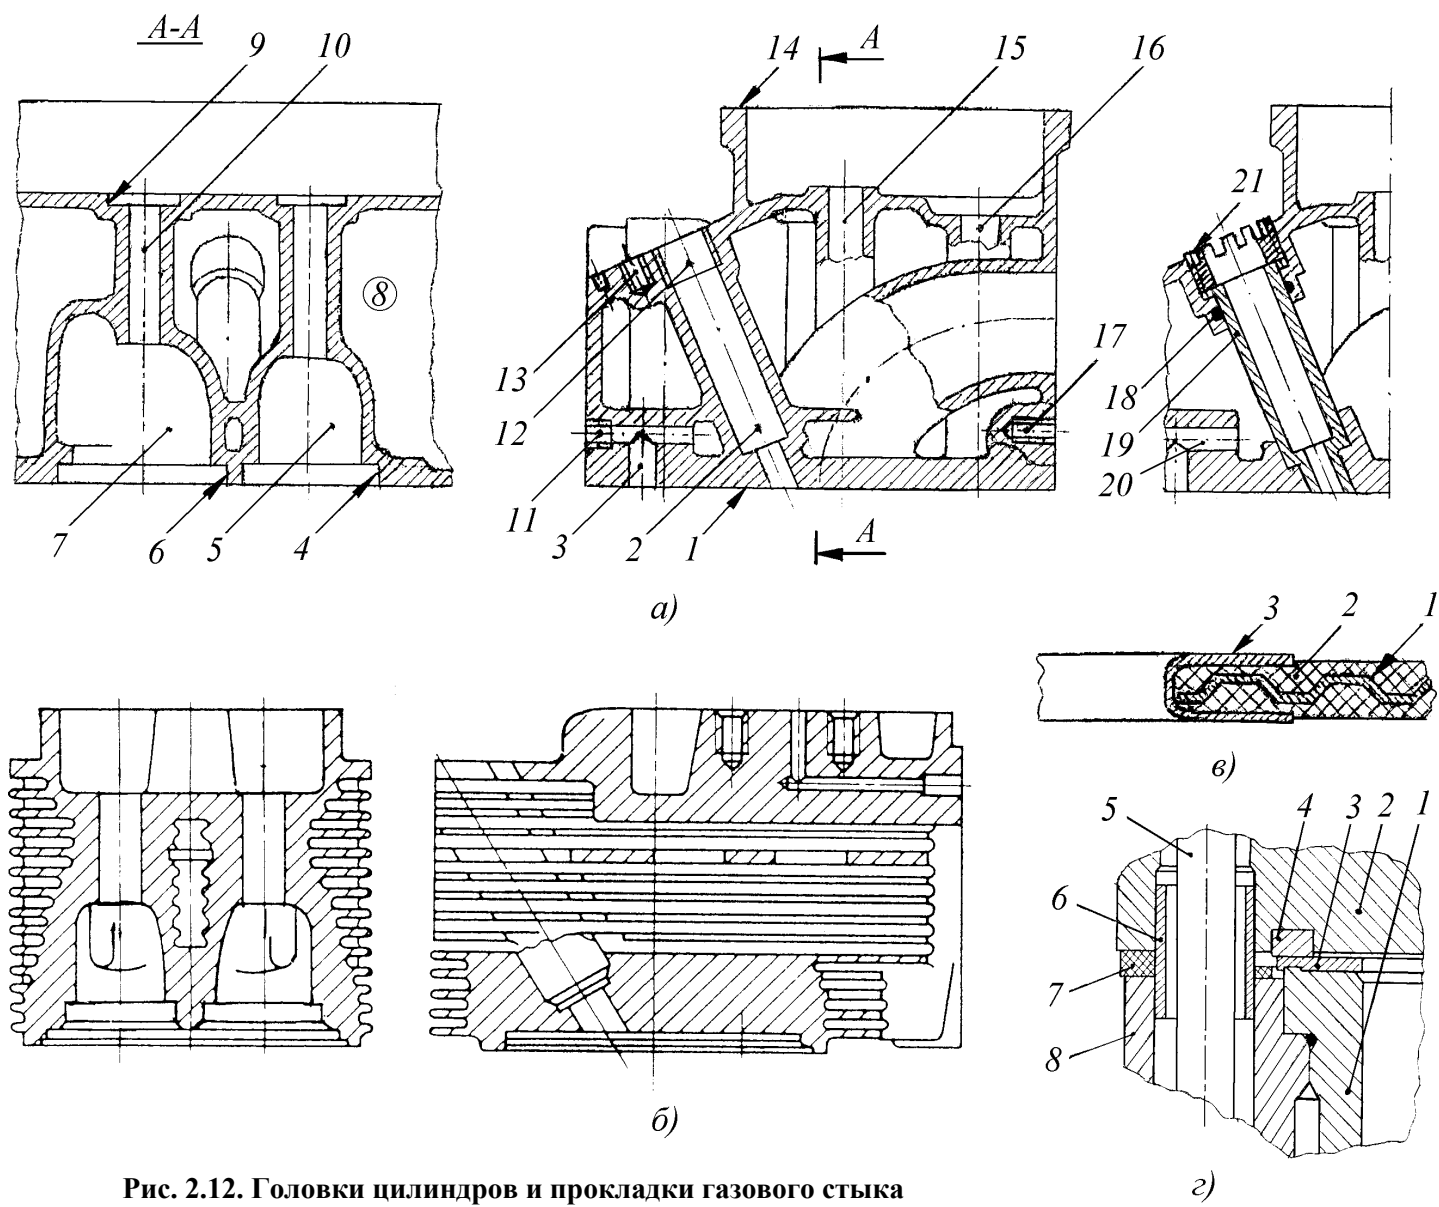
Головки цилиндров и прокладки газового стыка
